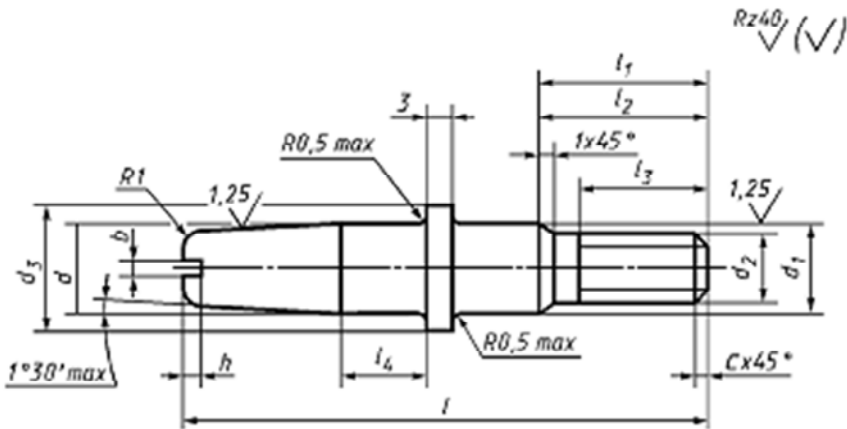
Конструкция центрирующих штырей с резьбовым хвостовиком
